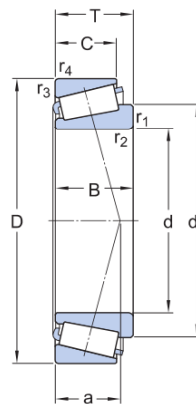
Geometría rodamiento rodillo cilíndrico 33108 [42]
